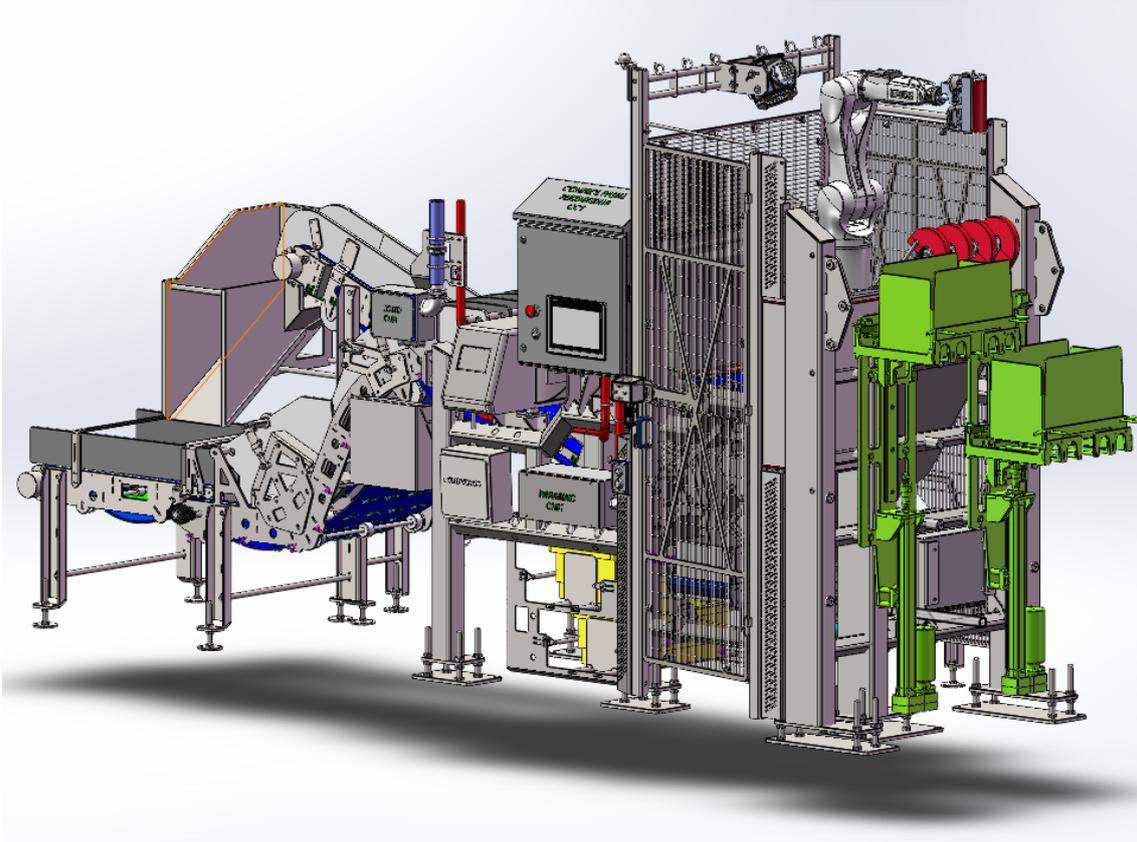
Elevadores (en color verde) unidos a la estructura principal de la RPS26
